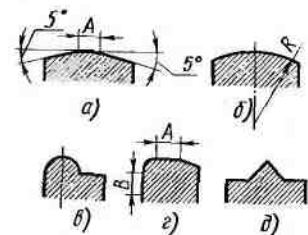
Профили роликов для обкатывания наружных поверхностей
